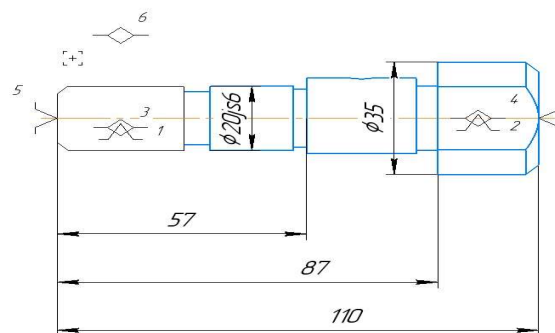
Базування деталі при токарній обробці по правому торцю
